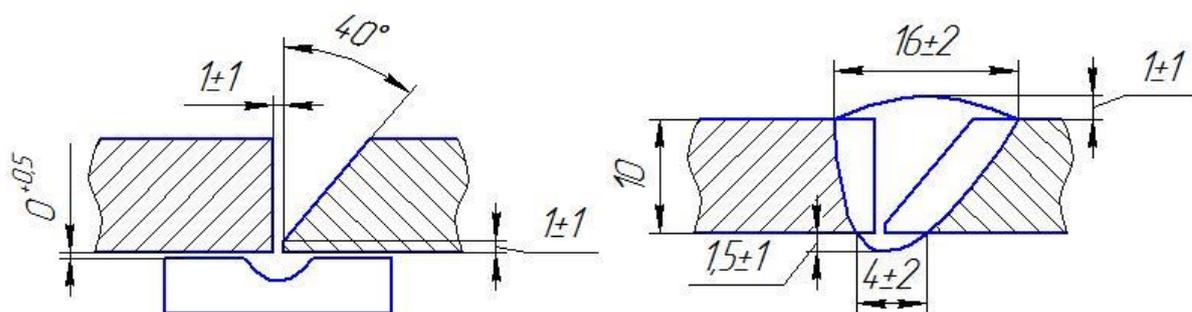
Разделка кромок и параметры шва (условное обозначение – С9)
